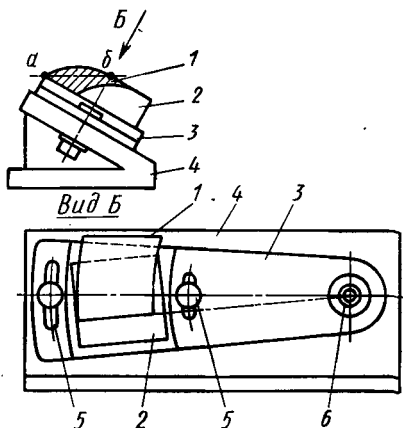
Схема приспособления для обработки наружного профиля направляющей лопатки под радиальным углом при повернутом положении лопатки
